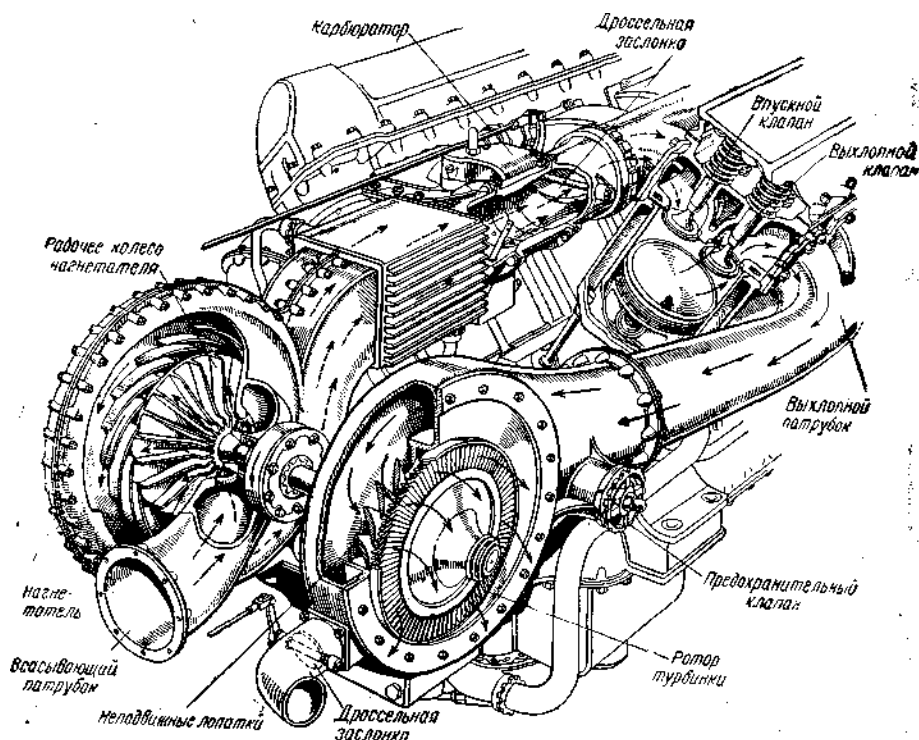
Установка турбокомпрессора на V-образном двигателе
